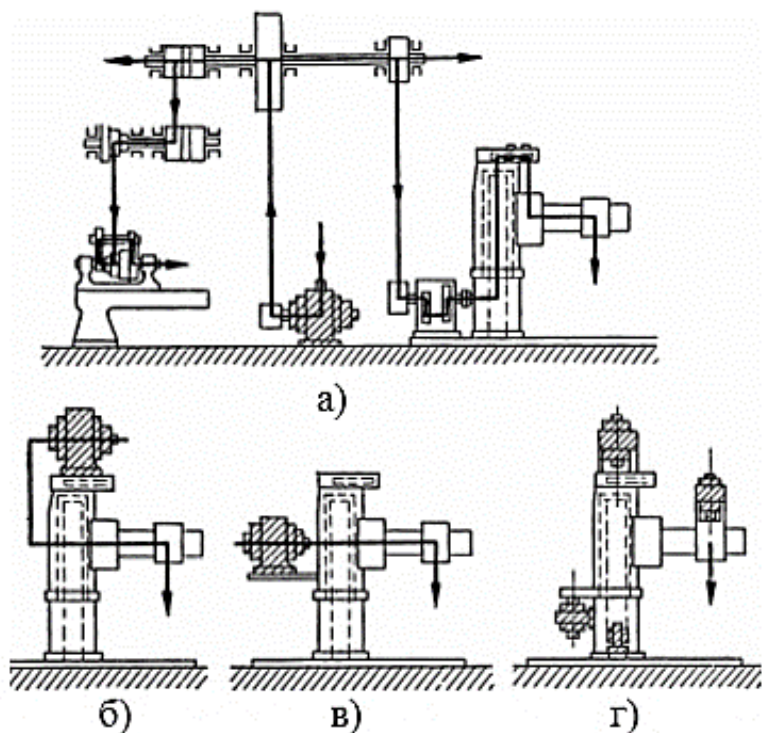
Схема розвитку електричного приводу радіально-свердлильного верстата
